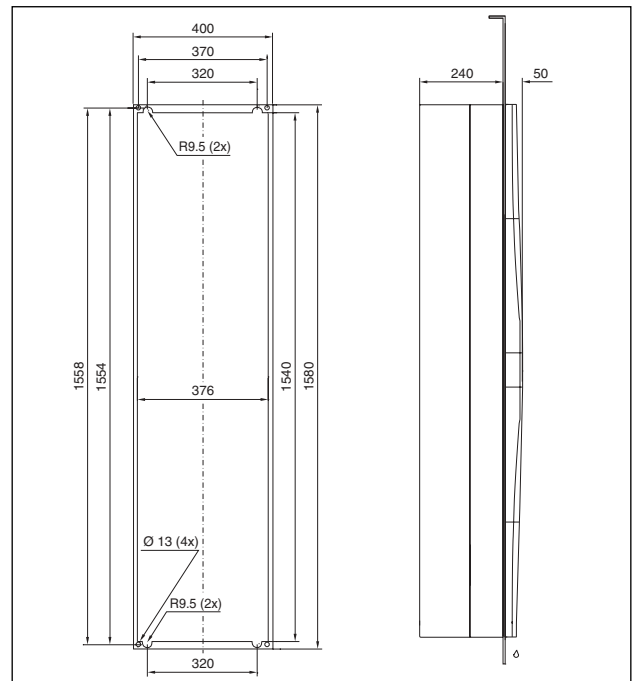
SK 3328.xxx, SK 3329.xxx Komplet inbyggnad
